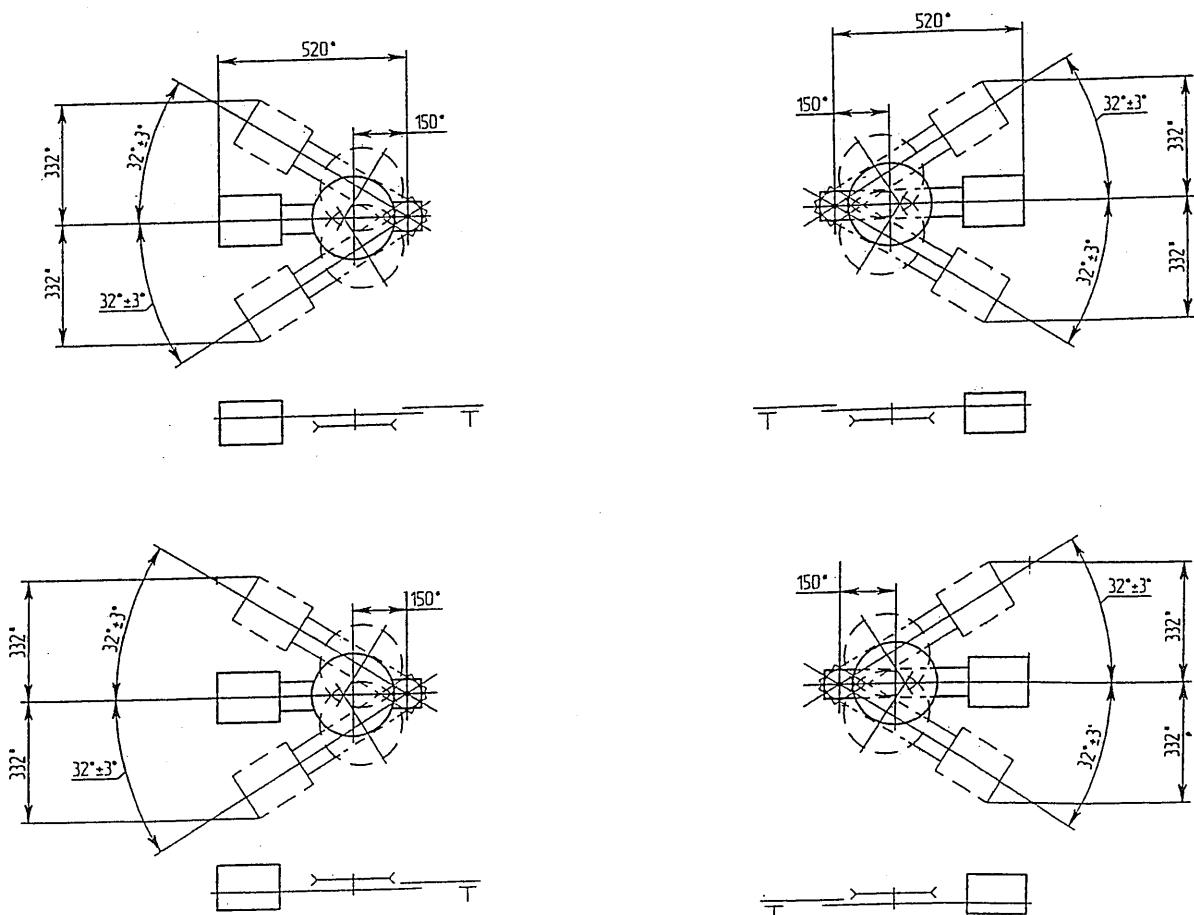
схемы сборок натяжного устройства каната ОС
